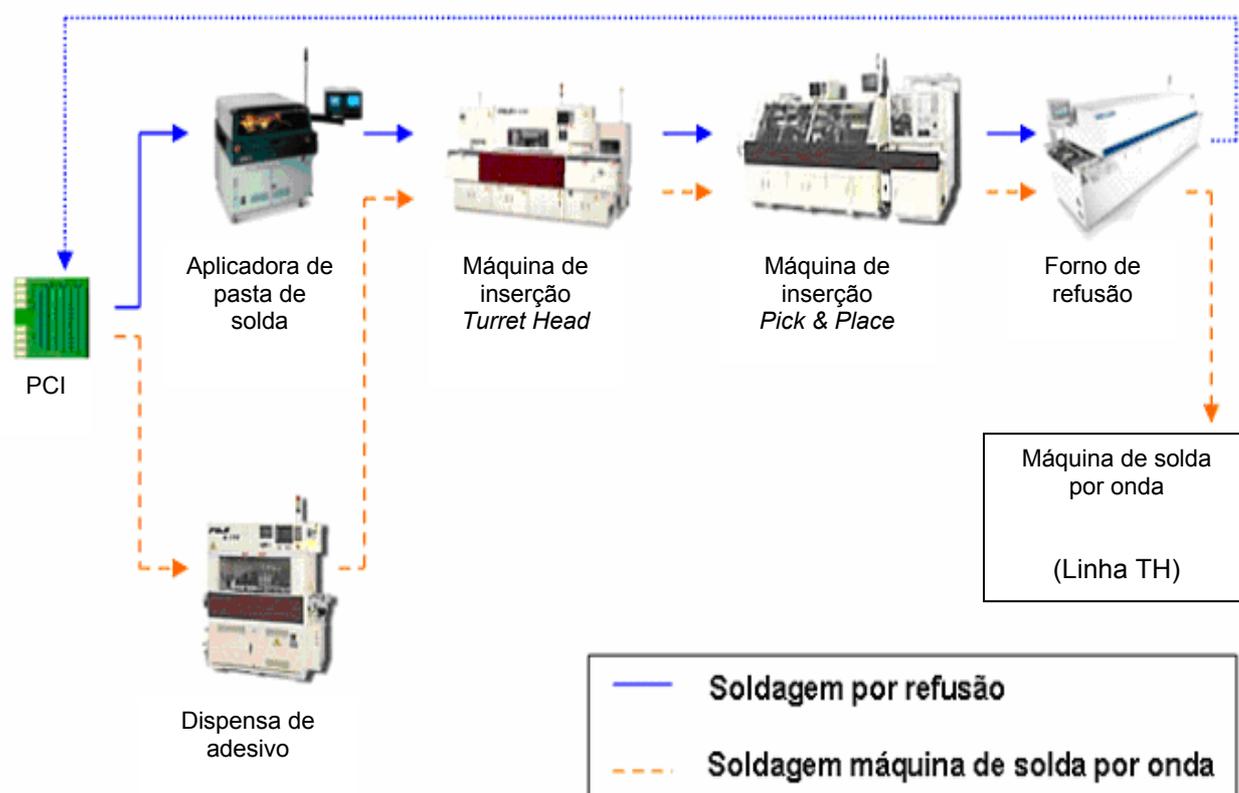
Equipamentos que compõem uma típica linha de montagem SMT
